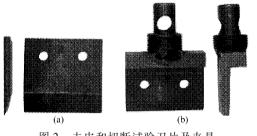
去皮和切断试验刀片及夹具 Fig. 2 Peeling and cutting test blade and fixture
